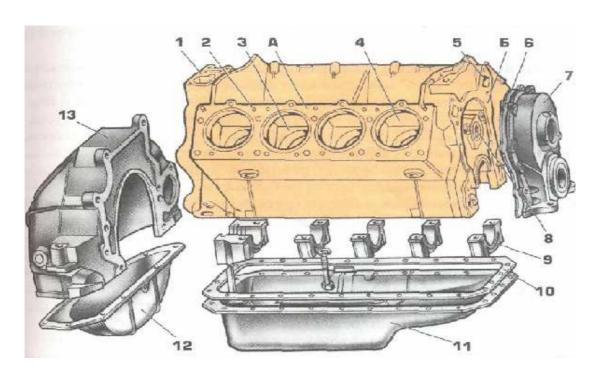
Корпусные детали двигателя ЗИЛ-508
